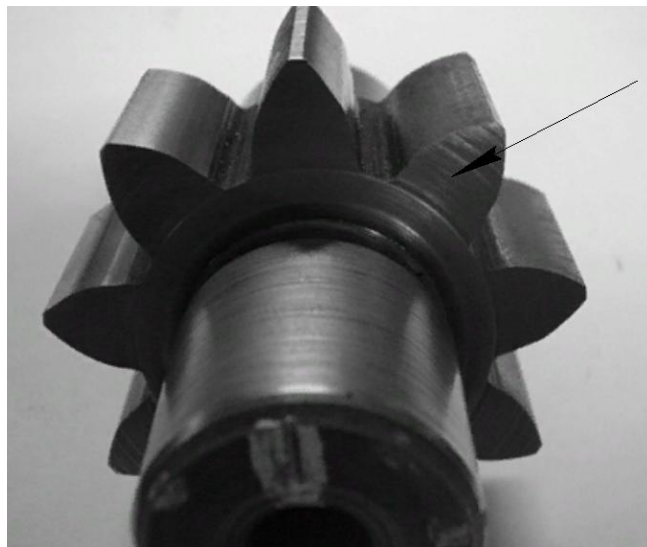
Зовнішній вид зносу торцевої поверхні шестерні
